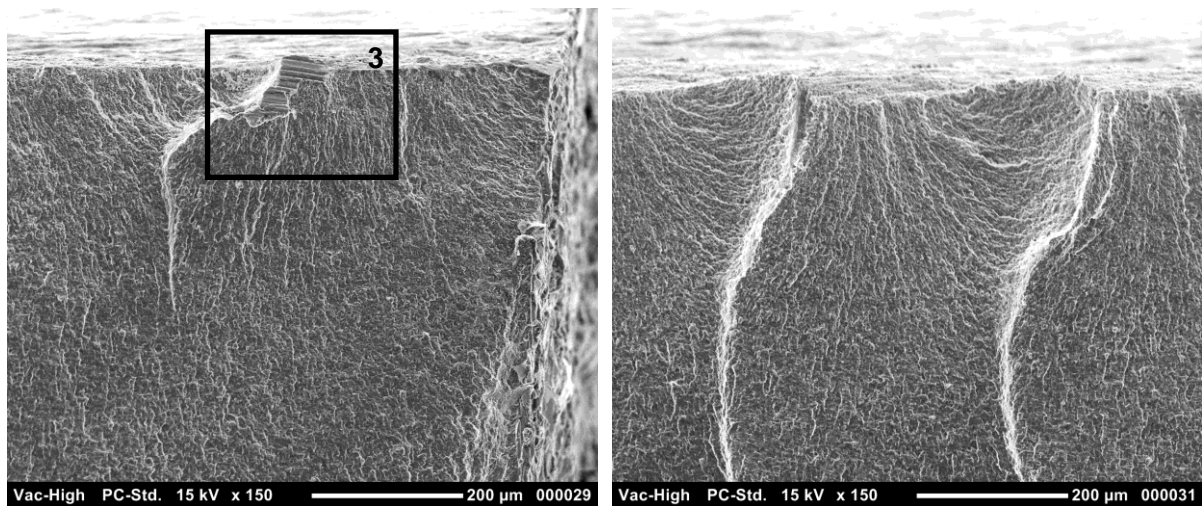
Übersichtsaufnahme der Bruchoberfläche einer Schweißung des Parametersatzes IMWF-13-00010 ($n=2000 \text{ min}^{-1}$, $v_x=750 \text{ mm/min}$, oben liegendes Blech, $a_1=3,5 \text{ mm}$)
